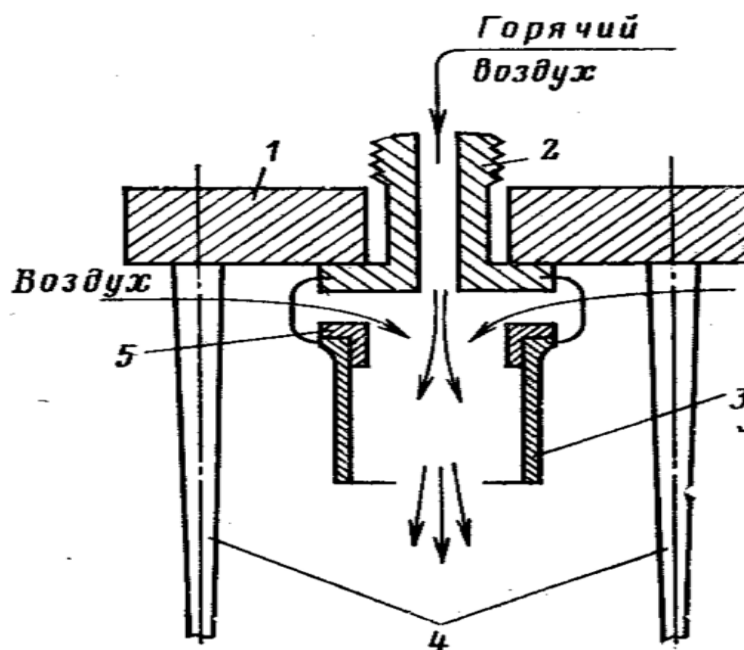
Схемы фильеры для формирования полого волокна из пластифицированного триацетата целлюлозы: 1- корпус фильеры; 2 - полый болт; 3 - насадка Вентури; 4 - полые струйки формовочной 5 - кольцо
